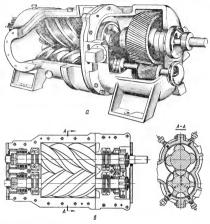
Винтовой компрессор: a - общий вид; 6 - разрезы.
